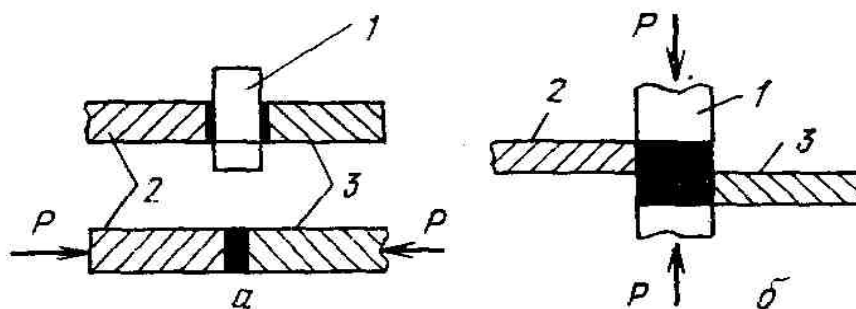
Схеми контактеного зварювання оплавленням (а) і проплавленням (б)
